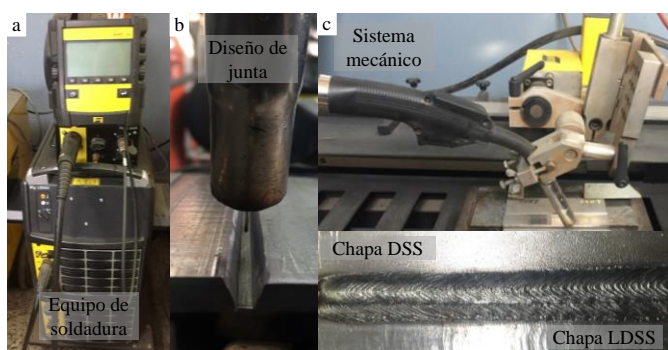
a) Equipo de soldadura, b) diseño de junta, c) sistema mecánico
